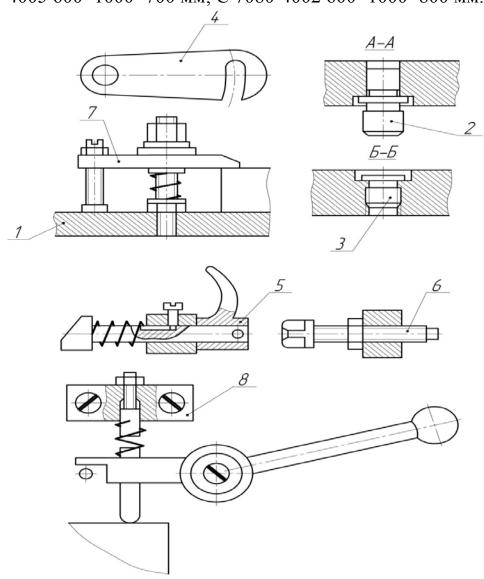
Комплект элементов, из которых компонуют модульные приспособления: 1 — базовая плита; 2 — базирующий штырь; 3 — пробка; 4 — защелка; 5 — курковый прижим; 6 — регулируемый упор; 7 — зажимное устройство; 8 — горизонтальный прижим с рукояткой
